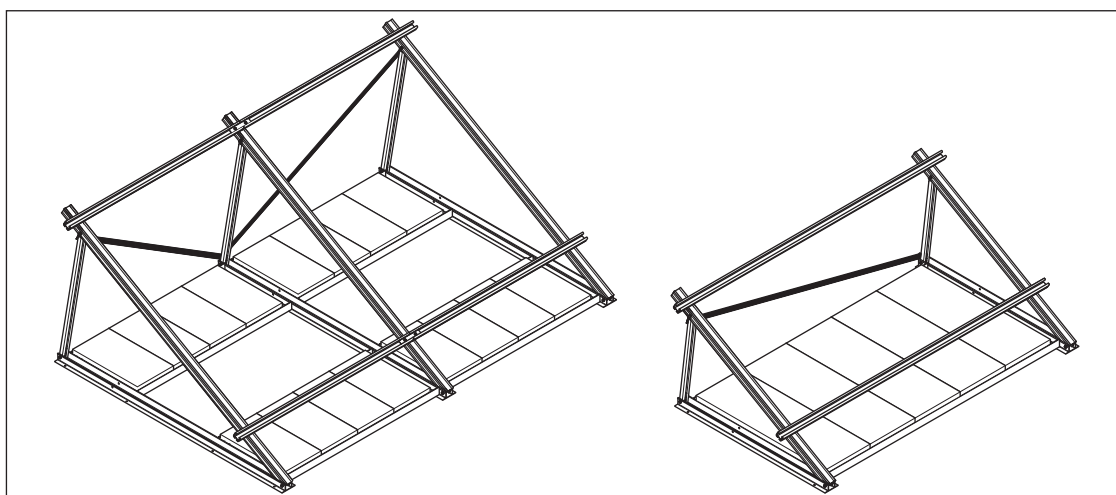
Fixation de la construction sur toit-terrasse en porte-à-faux au moyen de lests
